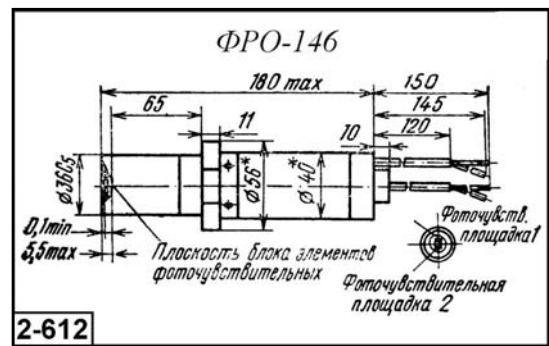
Внешний вид и габаритные размеры фоторезистора ФРО-146
